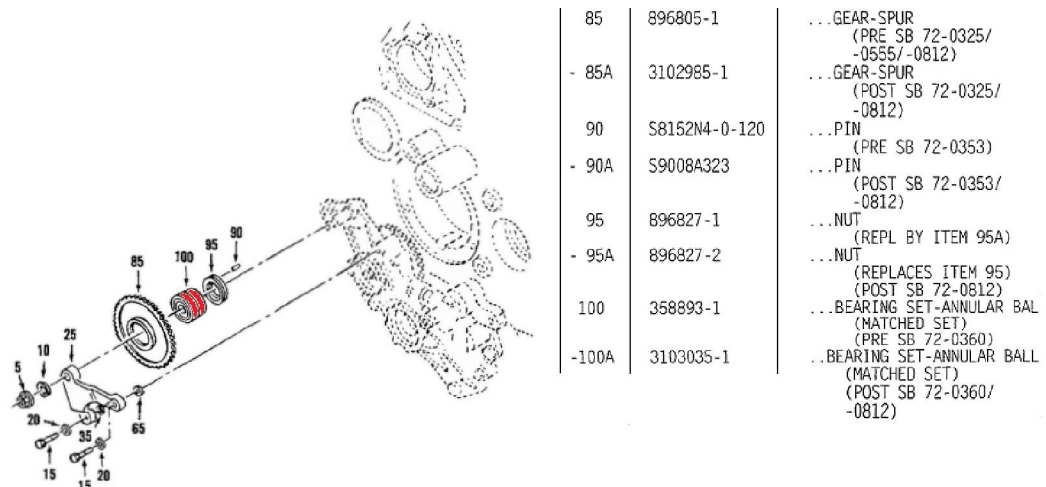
Ensamblaje de Generador de taquímetro y sensor de torque Previo al SB 72-0232 (resaltado en rojo sobre el dibujo la primer versión del rodamiento en cuestión).
